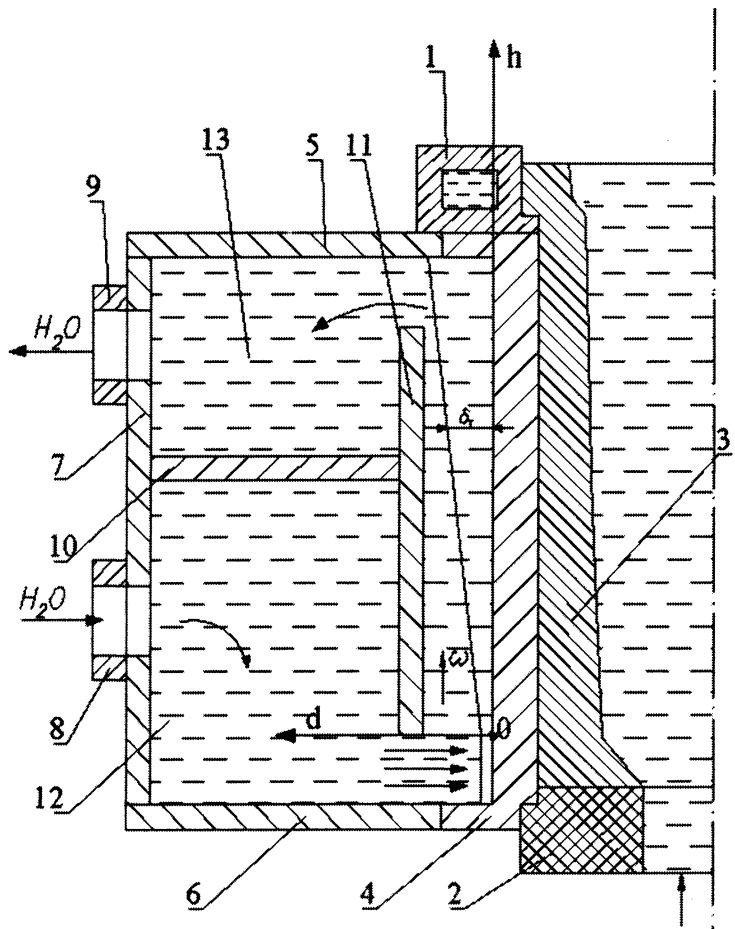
Работа обычного кристаллизатора: 1 – подвижный кристаллизатор; 2 – соединительный стакан; 3 – отливка; 4 – рубашка; 5 – верхний фланец; 6 – нижний фланец; 7 – корпус; 8 – подводящий патрубок; 9 – отводящий патрубок; 10 – перегородка; 11 – экран; 12 – нижний коллектор; 13 – верхний коллектор
